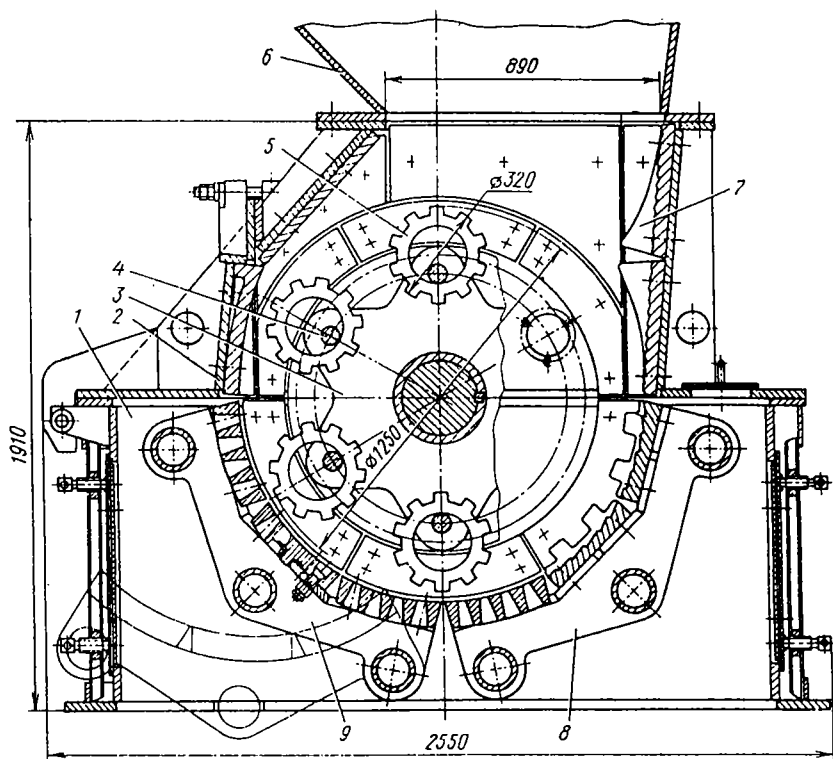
Однороторная молотковая стружкодробилка СМД-135
